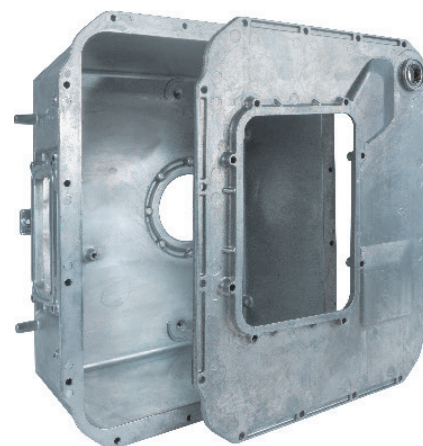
Gehäuse aus Zinkdruckguss für die Röntgen-Dentaltechnik.
